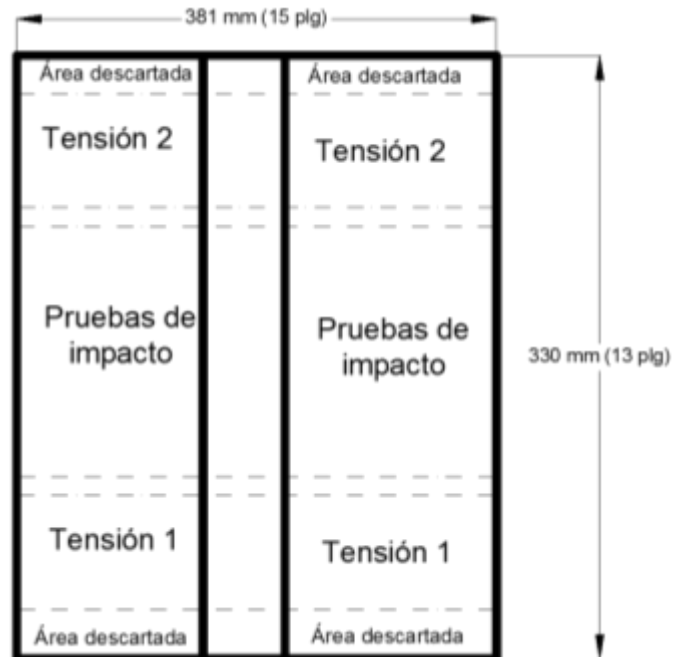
6 Representación esquemática del seccionamiento del cupón realizado con soldadura húmeda utilizando el proceso MMAW.
